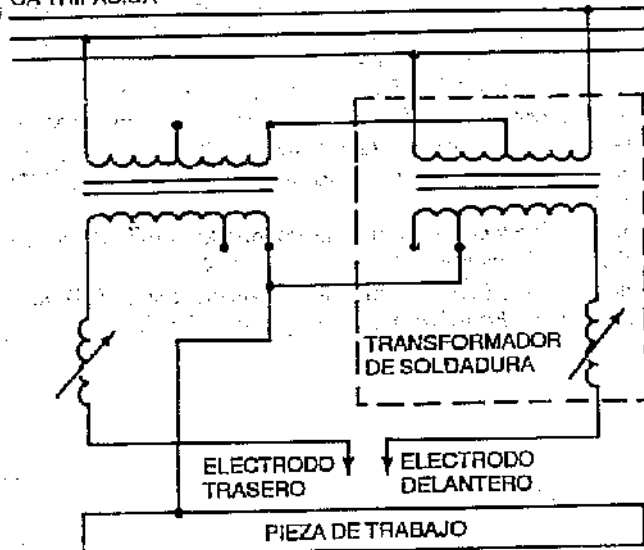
Conexiones de transformador para soldadura con arco con un sistema de conexión Scott
